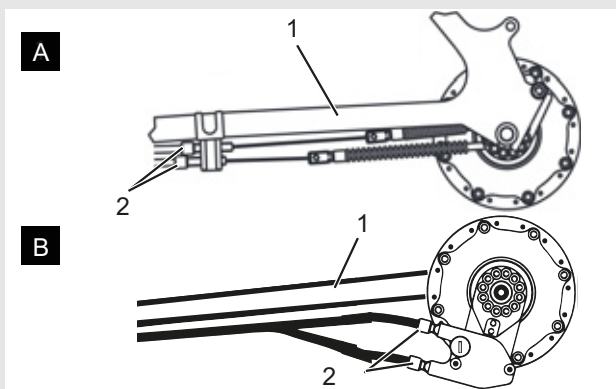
Slutmuffe (1) på gearsiftet med ét kabel og gearvælgerhus (2), eksempel
